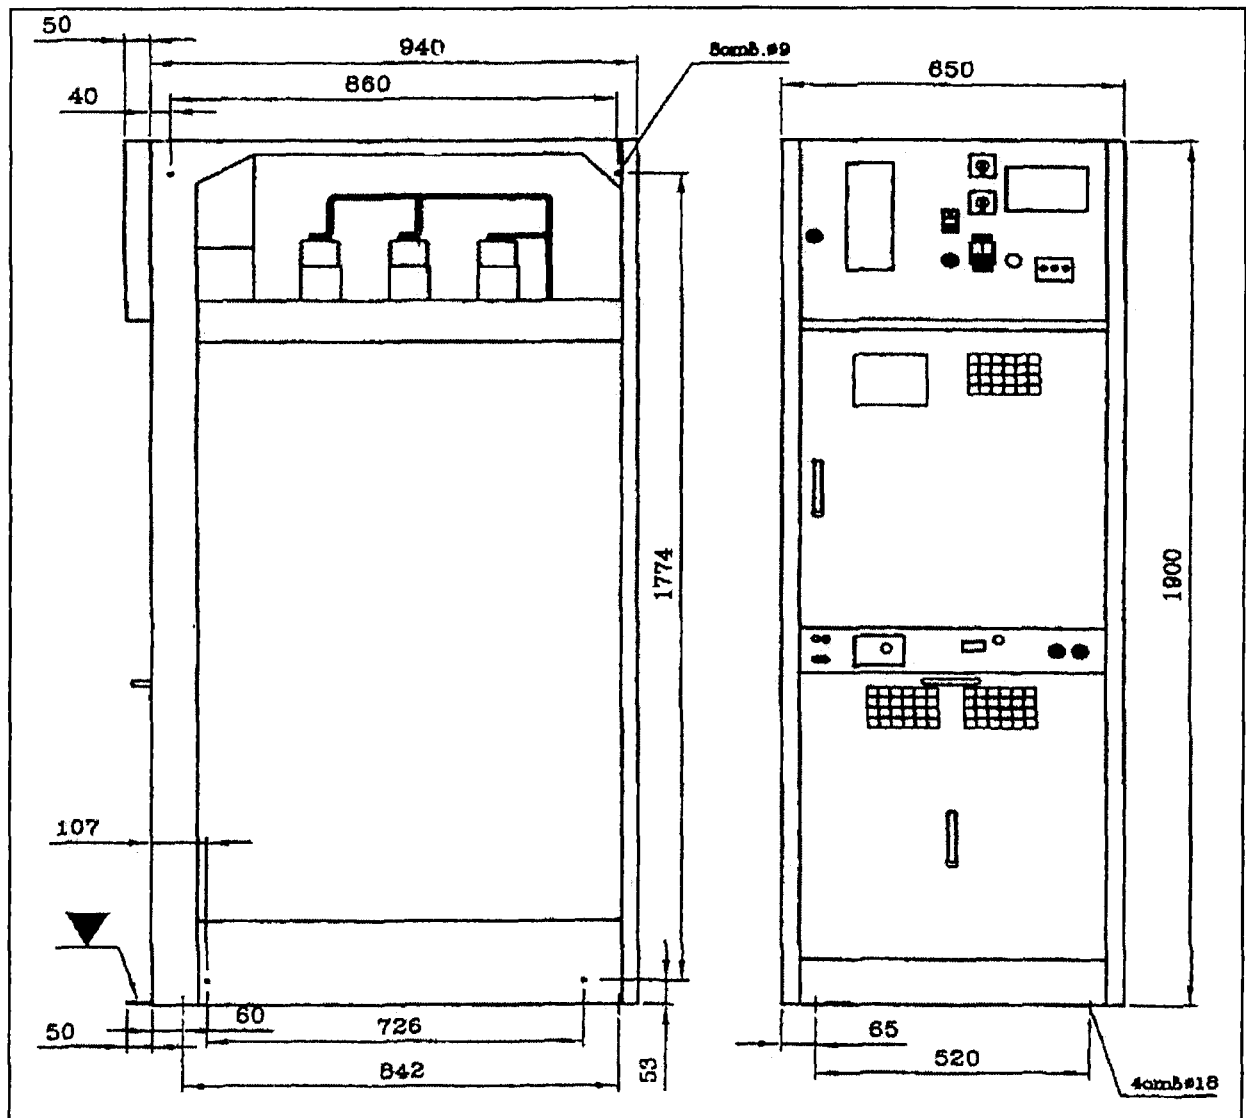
Общий вид и габаритные размеры камеры КСО 298 MSi
